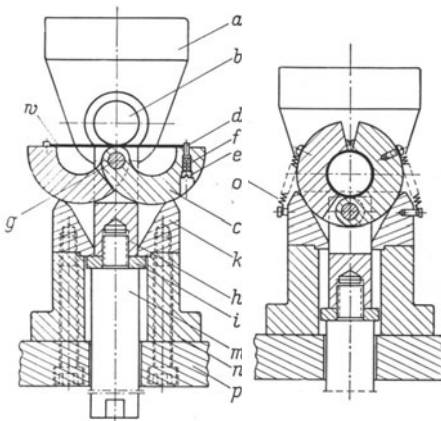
Umrollbiegewerkzeug mit Schwenkbacken
